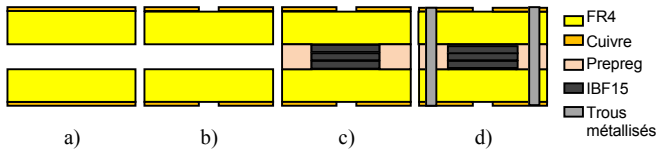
Processus de réalisation de l'inductance : a) PCB fin, b) pistes gravées, c) pressage du circuit magnétique entre les deux PCB, d) trous métallisés pour connecter les deux PCB
